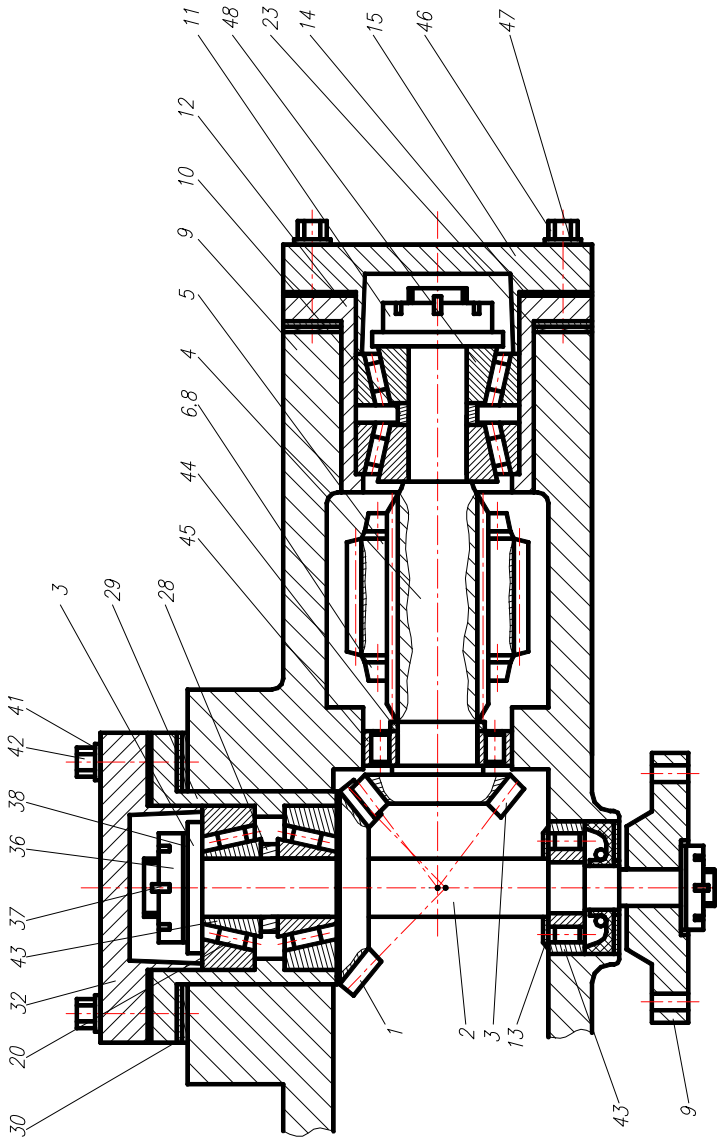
Устройство редуктора автомобиля ЗИЛ-131
